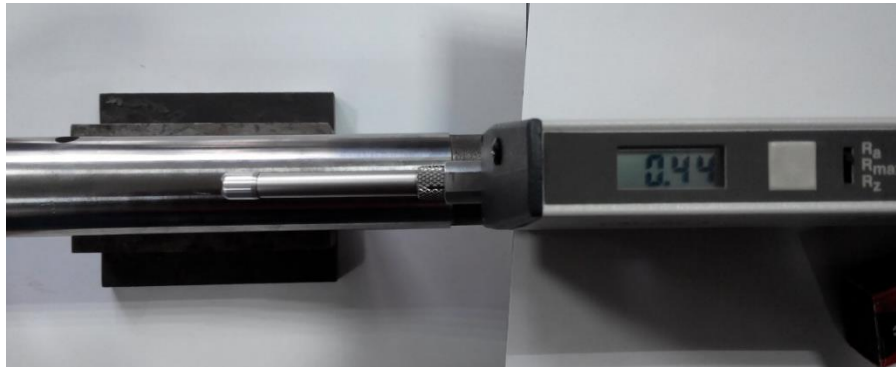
Процес вимірювання величини шорсткості циліндричної поверхні приладом PocketSurf III після обробки
